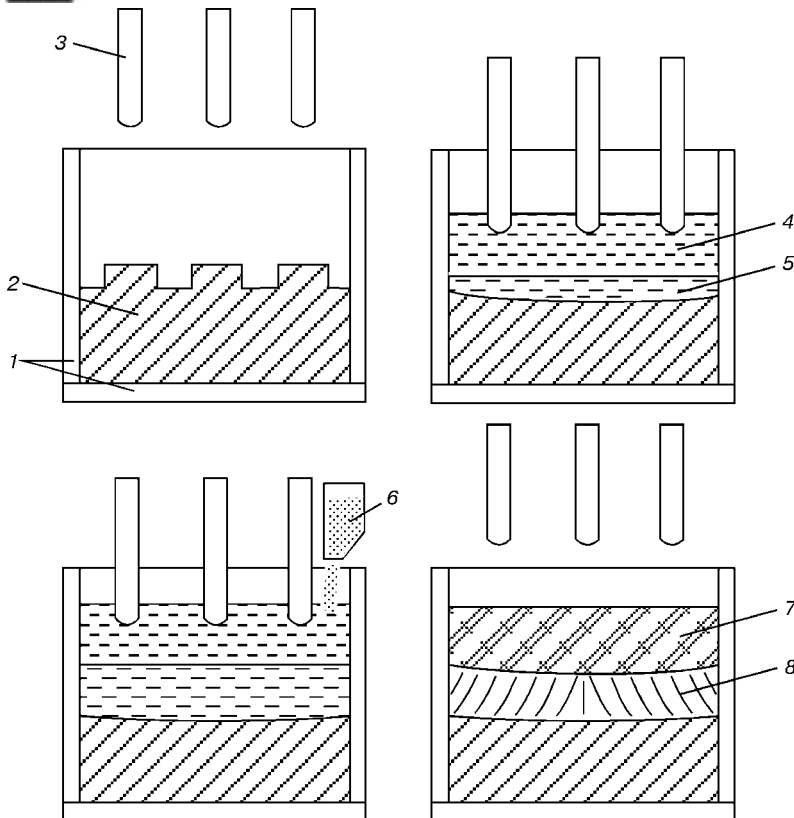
Схема электрошлаковой наплавки штампов: 1 — водоохлаждаемые панели; 2 — изношенный штамп; 3 — нерасходуемый электрод; 4 — шлаковая ванна; 5 — металлическая ванна; 6 — бункер со стружкой; 7 — твердый шлак; 8 — наплавленный слой
